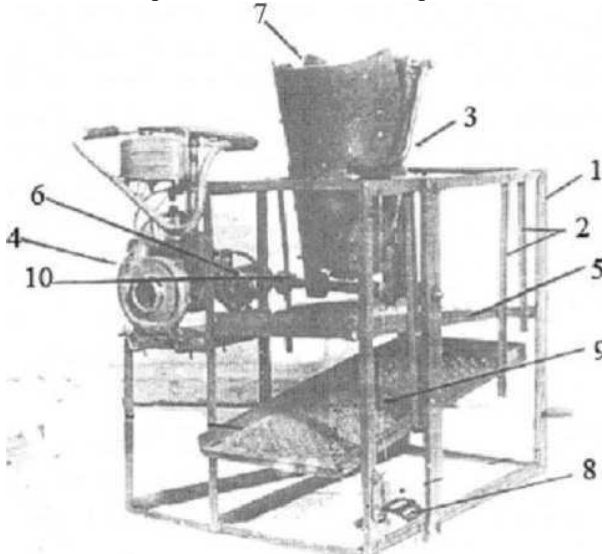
Загальний вид шишко-подрібнювача Попова А.Т.: 1 - корпус, 2 - підвіски для кріплення решіт, 3 - дробильний агрегат, 4 - бензомоторна пилка, 5 - верхнє сито, 6 - редуктор пилки, 7 -
